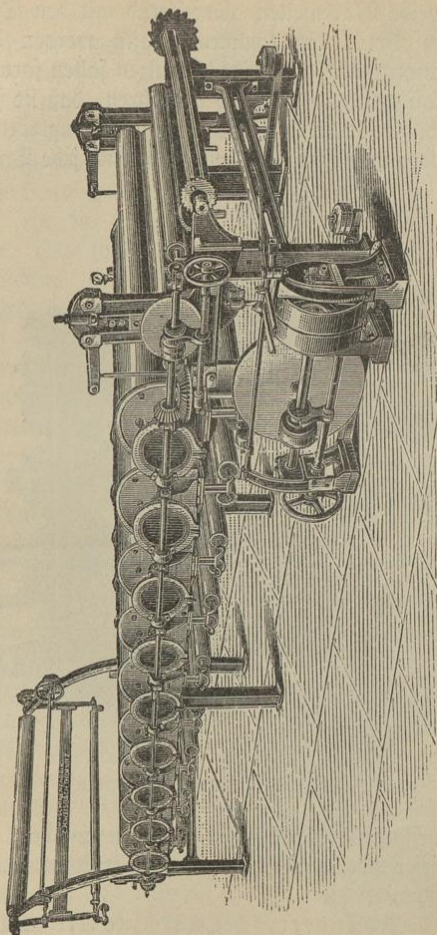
Zylinderdrottenmaschine mit neun Zylindern.
